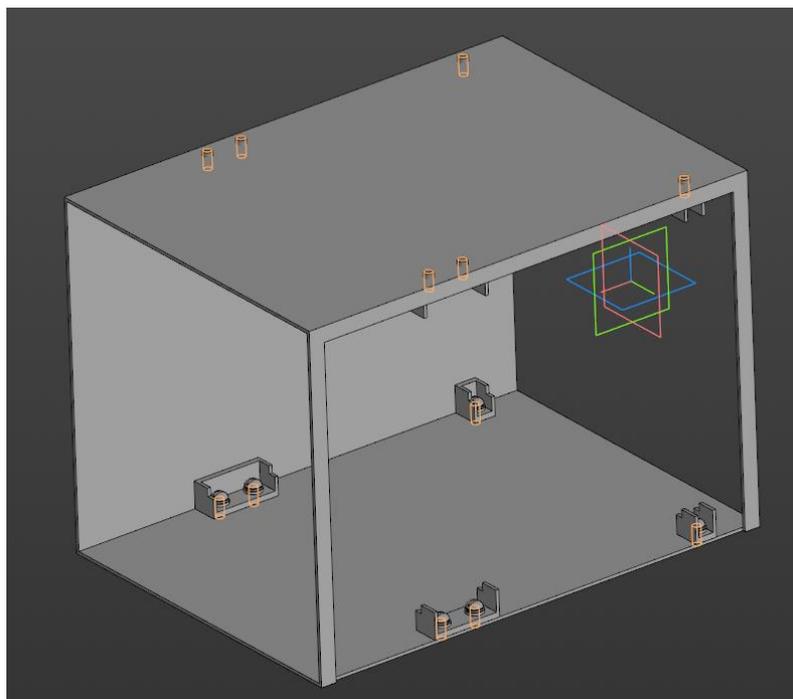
Корпус с установленными внутри крепежами для фильтрующих элементов
